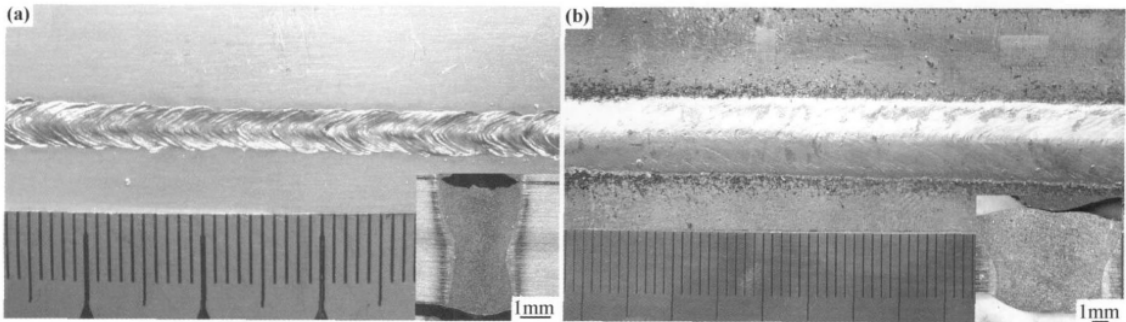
激光焊(a)与复合焊(b)的焊缝形貌
